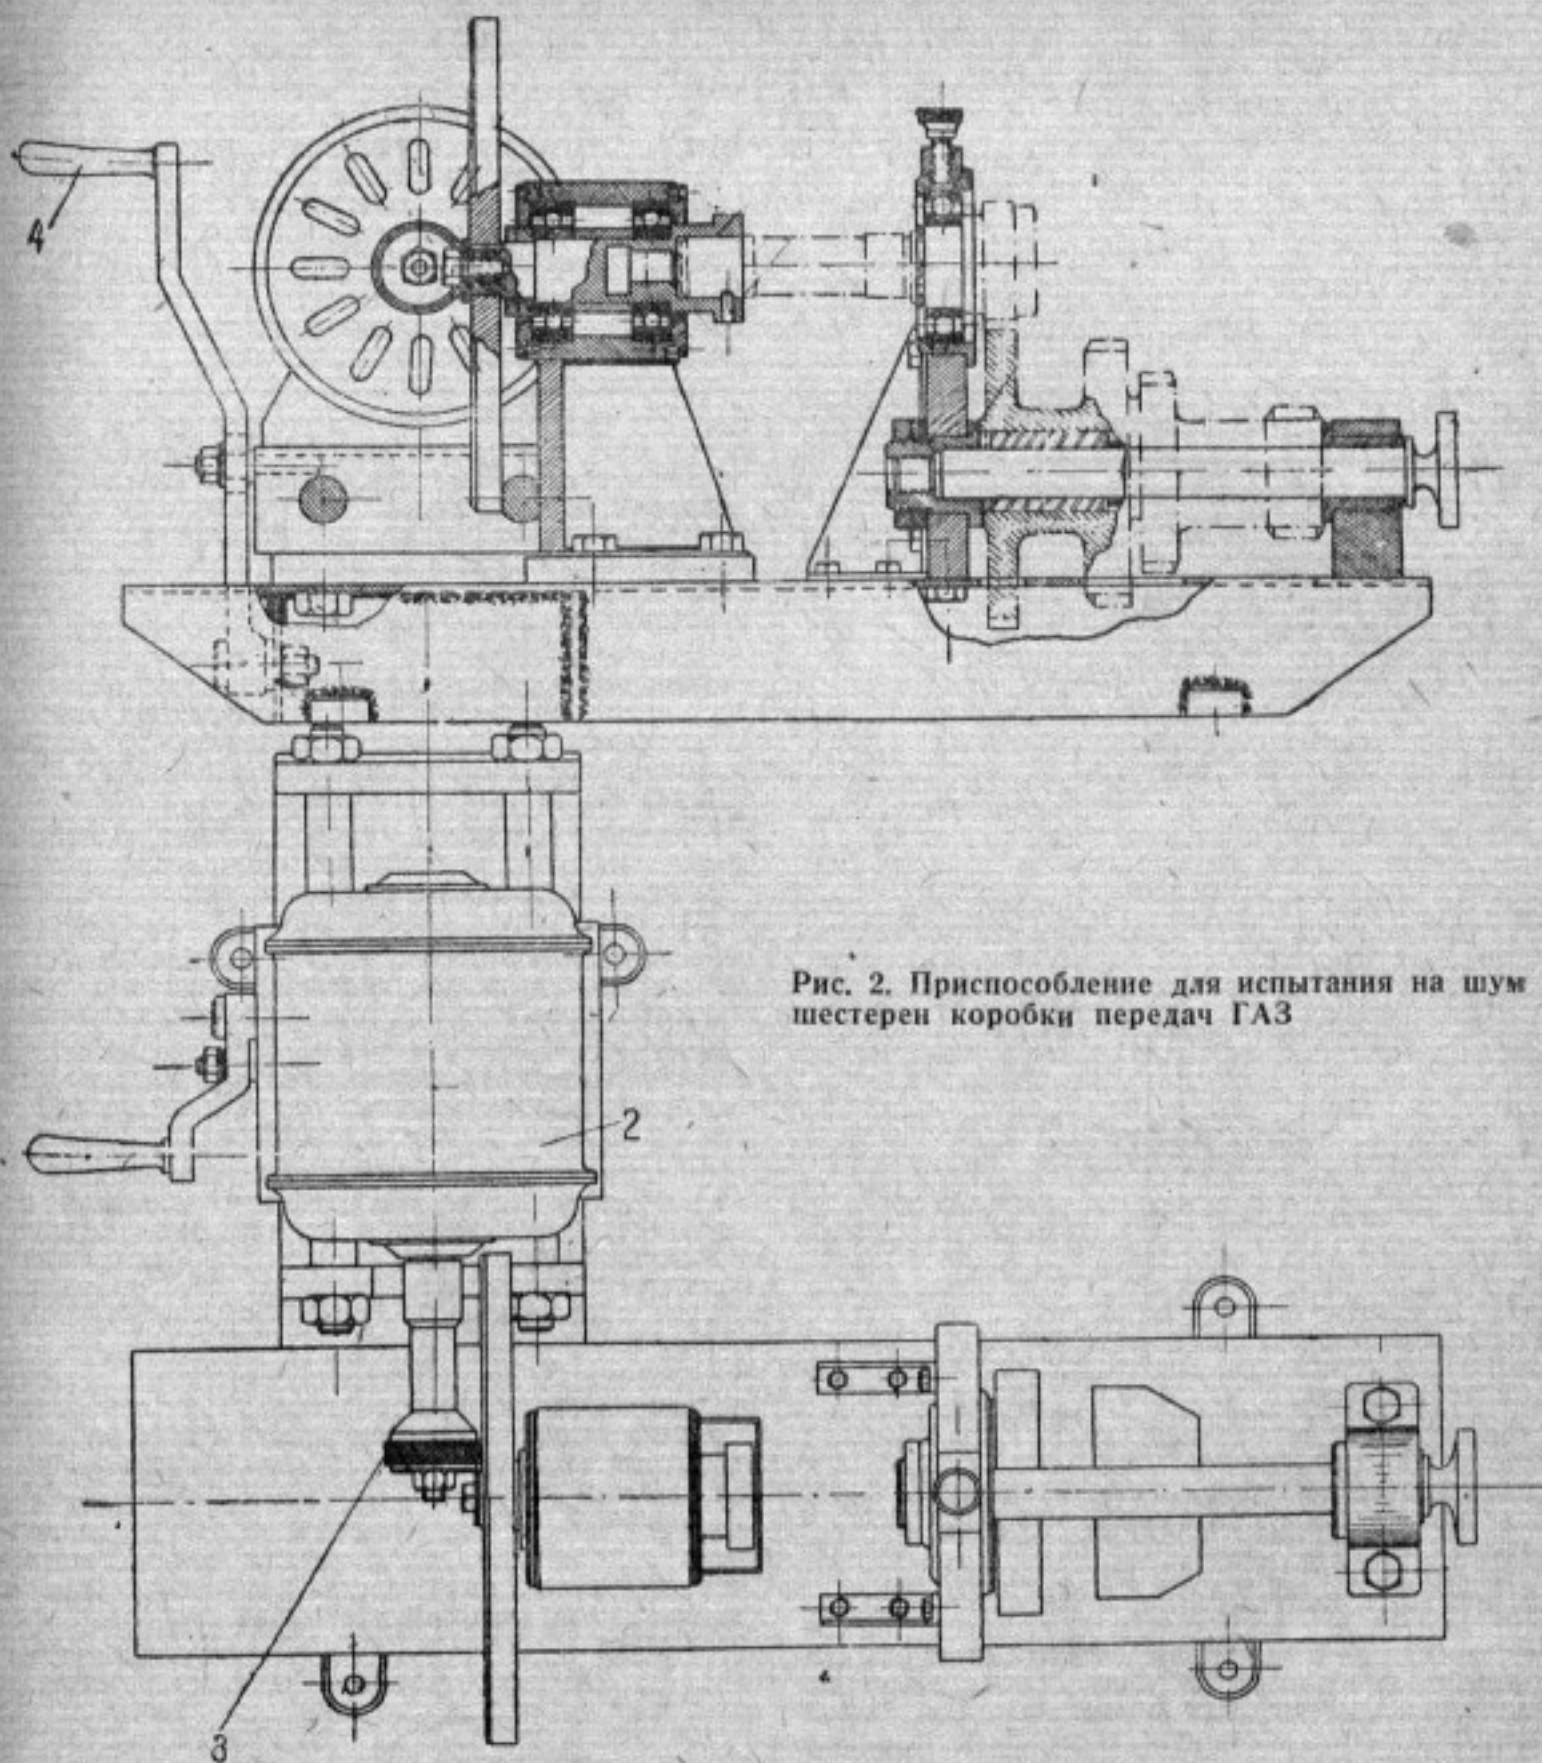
Приспособление для испытания на шум шестерен коробки передач ГАЗ
